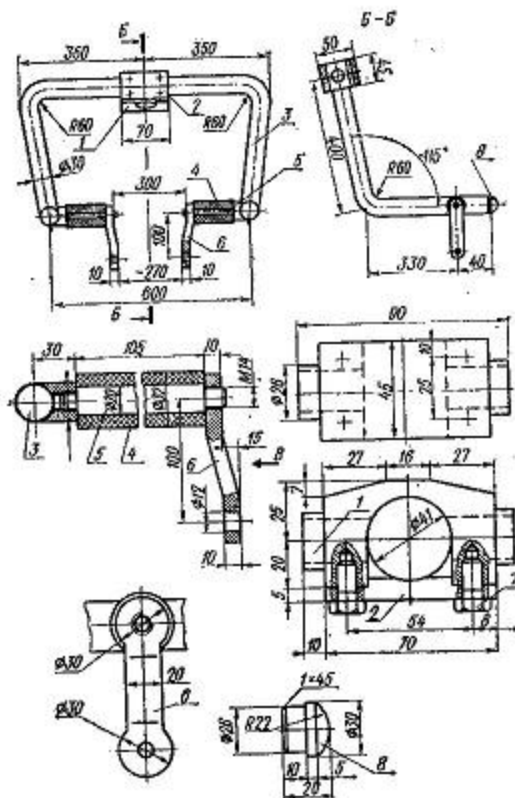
Дуги ограждения для мотоцикла «ИЖ»: 1, 2 — хомут; 3 — дуга; 4 — подножка (резина); 5 — ось подножки; 6 — крошитель; 7 — болт; 8 — заглушка
